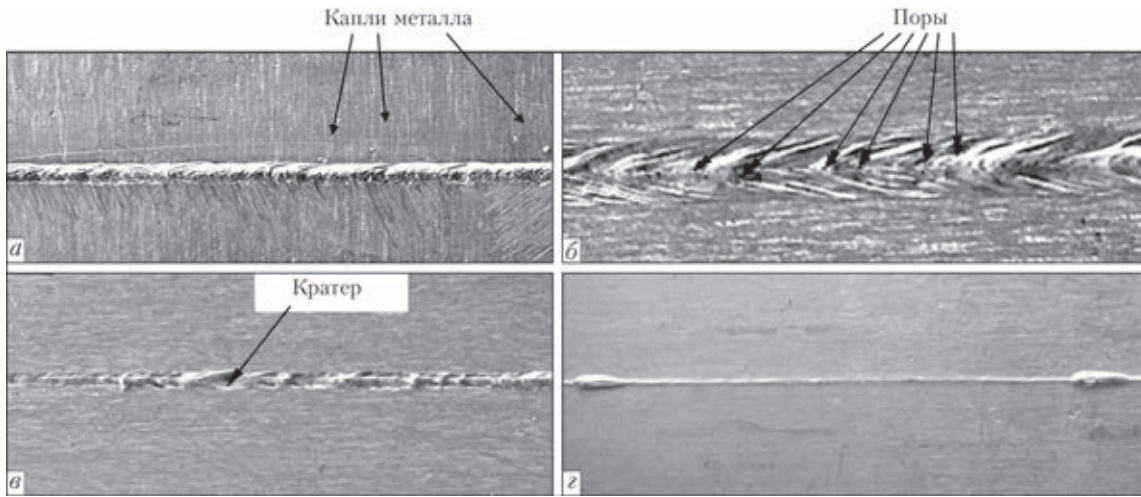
Внешний вид и характерные дефекты сварных соединений ($\times 3$): а-в — лицевая сторона; г — обратная
